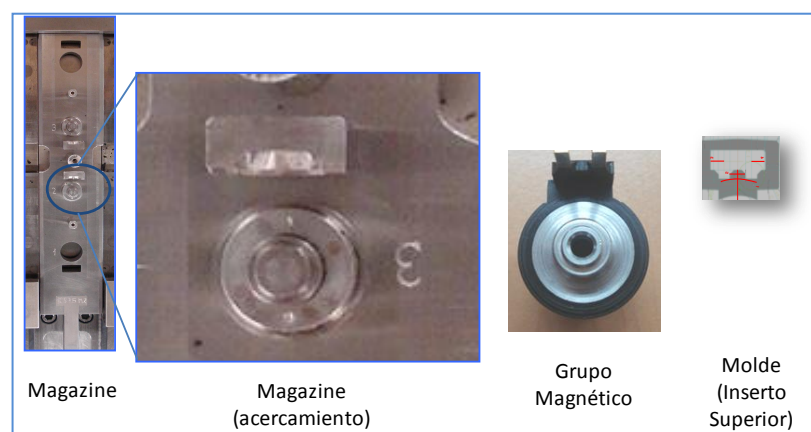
Elementos que interactúan durante la inyección del grupo magnético 326.
